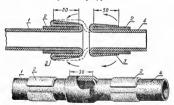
Стыковка камеры: 1 — камера; 2 — разрезные манжеты; 3 — прошерохованные и промазаные поверхности; 4 — вставка.
